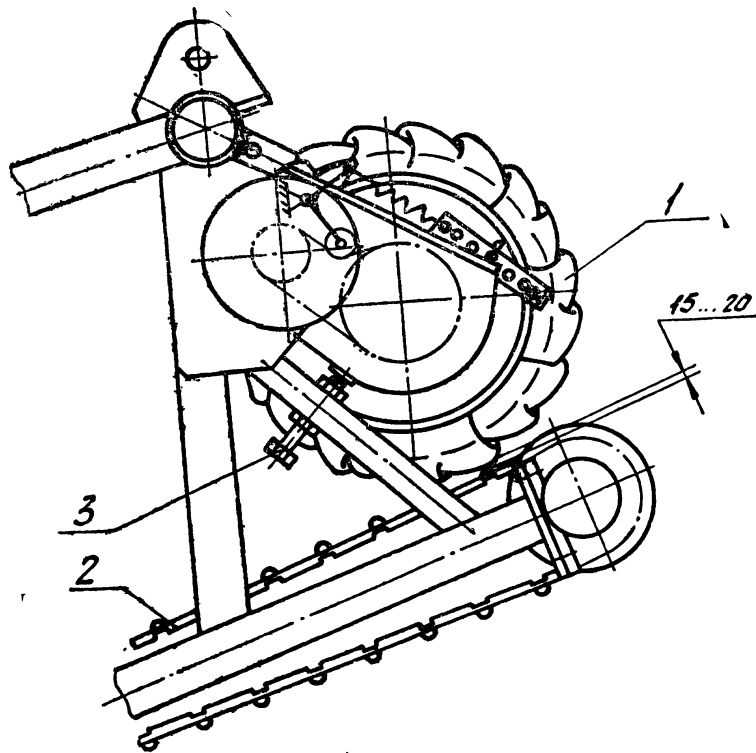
Регулировка интенсивности отделения примесей на основном элеваторе. Регулировка натяжения цепного контура: 1 - боковой шнек; 2 - прутки элеваторов; 3 - регулировочный винт
